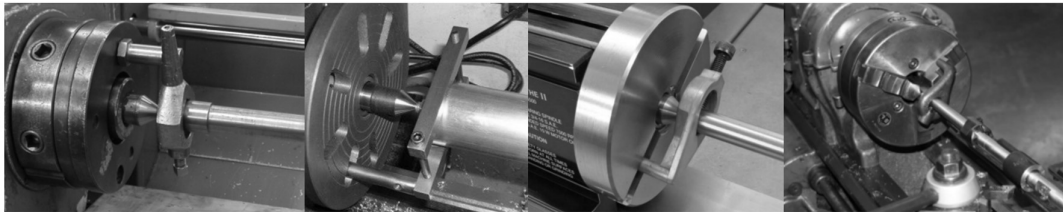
Exemplos de aplicações de diferentes conjuntos de placas de arrasto e *lathe dogs
